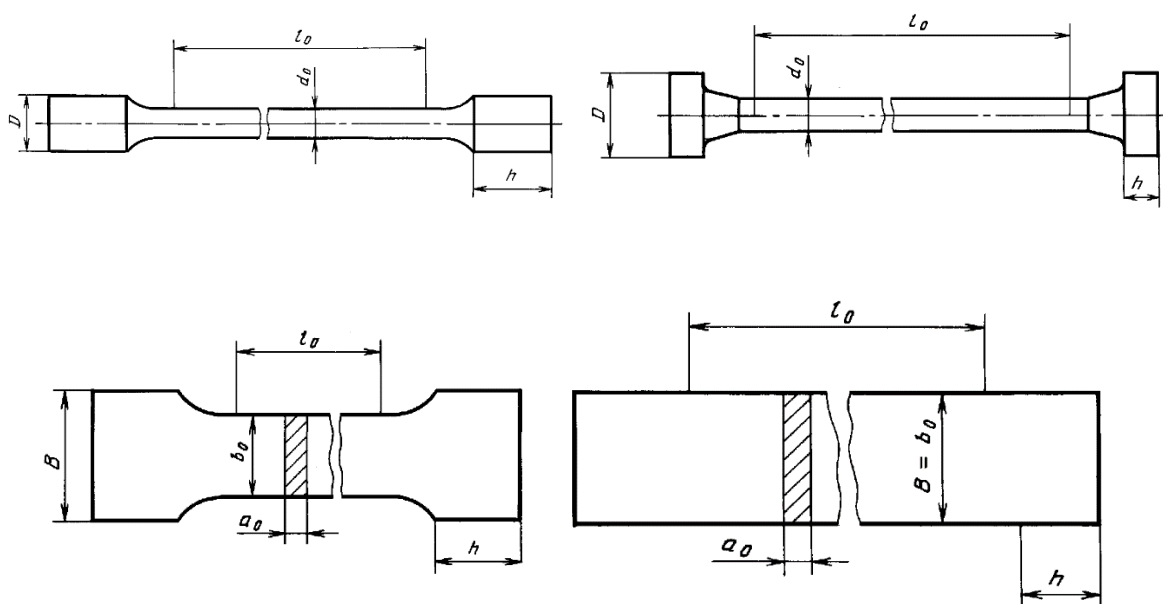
Примеры образцов для испытаний на растяжение цилиндрические (сверху) и плоские (снизу).
